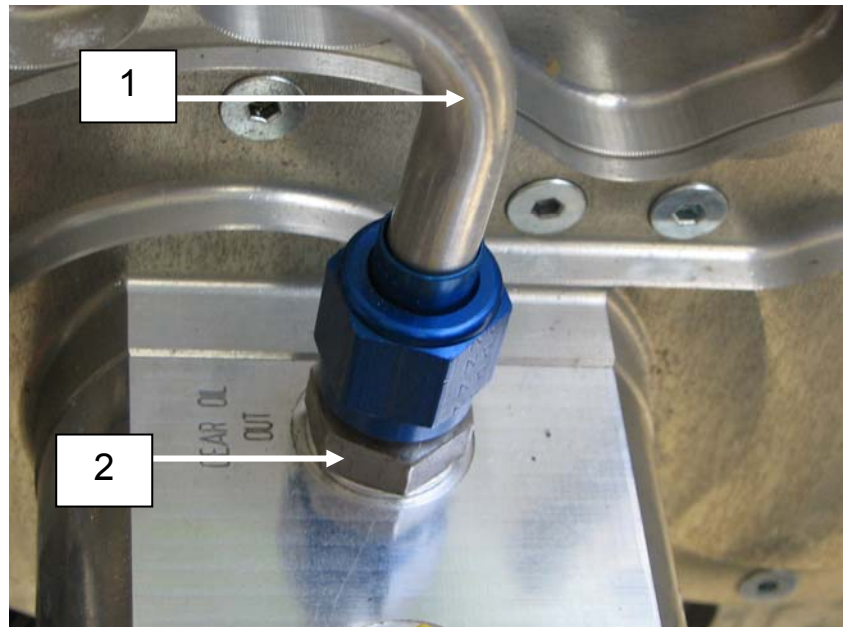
Aluminiumrohrleitung / Fig. 1 Pipe connection
